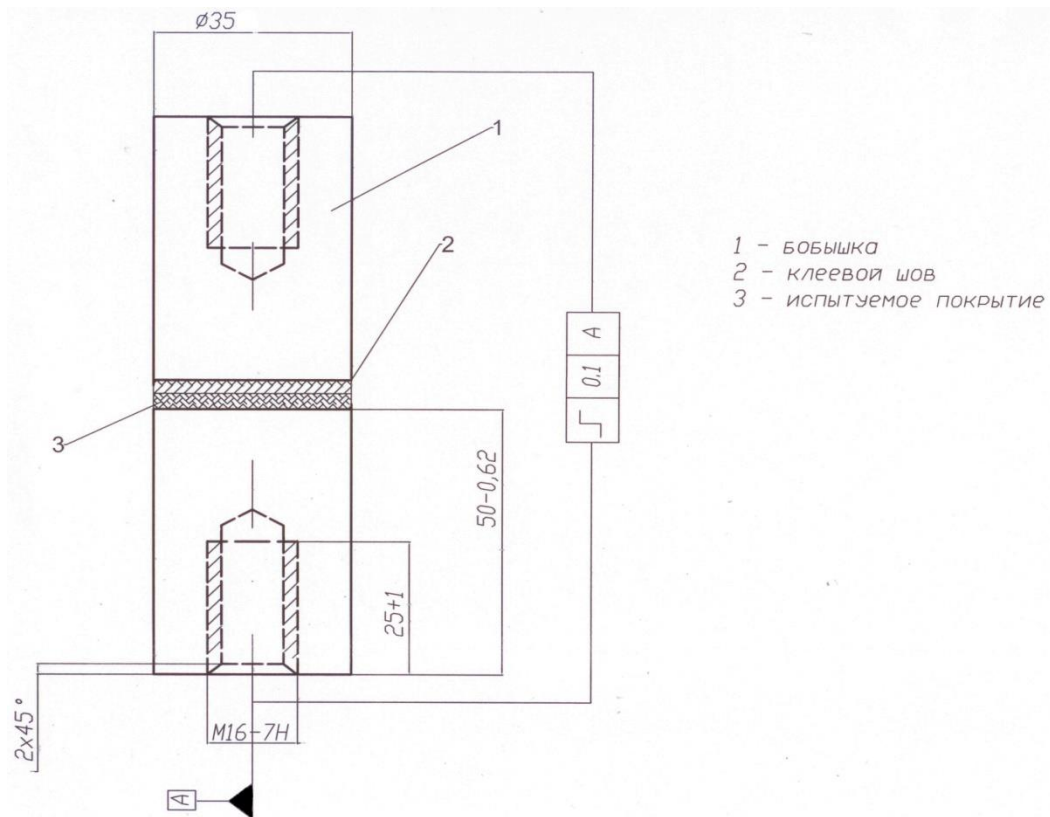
Образец для испытаний ТРП на металлической подложке
